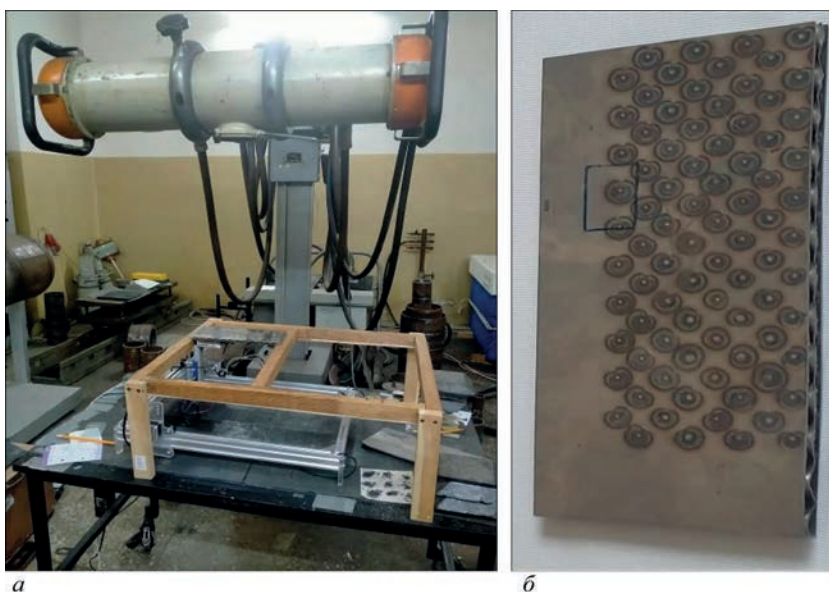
Процес 2D сканування зразка (а), зразок точкового зварного з'єднання трьох сталевих листів (б)
